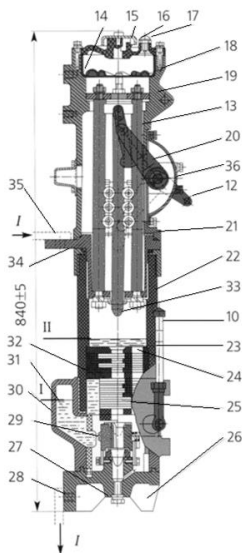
Разрез полюса выключателя ВМП-10: 13 - выпрямляющий механизм; 14 - маслоотделитель; 15 - канал для выхода газа; 16 - крышка; 17 - пробка маслоналивного отверстия; 18 - отверстия маслоотделителя; 19 - корпус; 20 - рычаг; 21 - контактный стержень; 22 - стеклоэпоксидный цилиндр; 23 - центральный канал камеры; 24 - боковой выхлопной канал; 25 - дугогасительная камера; 26 - нижняя крышка фазы; 27 - маслоспускная пробка; 28 - отводящая шина; 29 - неподвижный контакт; 30 - нижний фланец; 31 - буферное пространство; 32 - масляный карман; 33 - подвижный контакт; 34 - верхний
